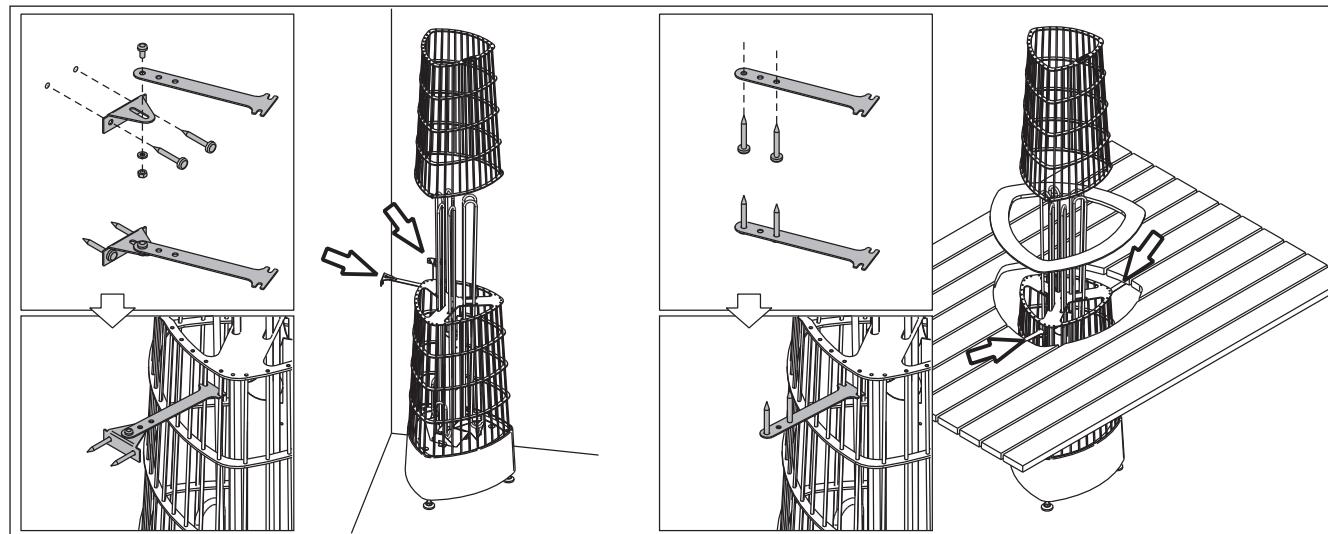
Установка нагревателя с помощью крепежных наборов
